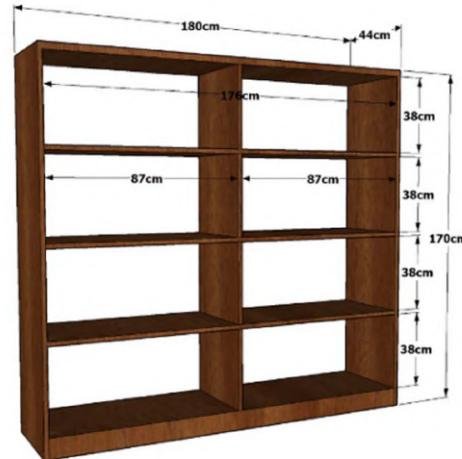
Rak buku tipe A di ruang perpustakaan umum lamongan
